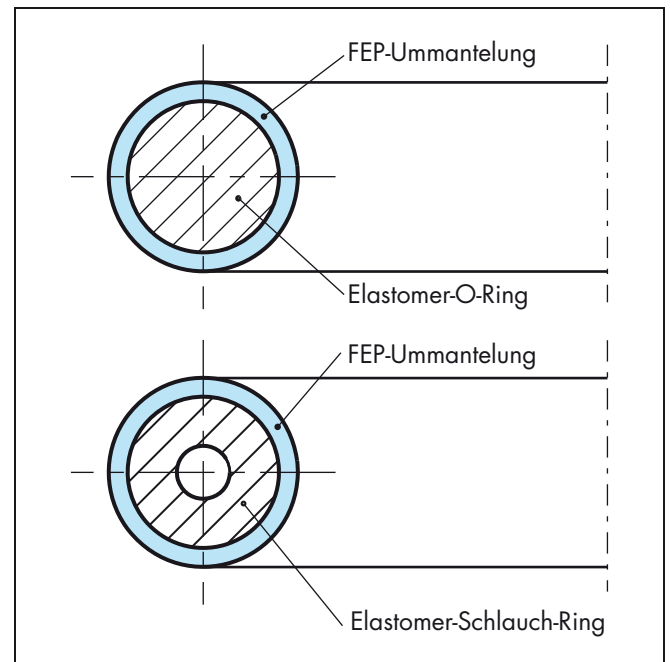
Ausführungen von FEP-ummantelten O-Ringen
